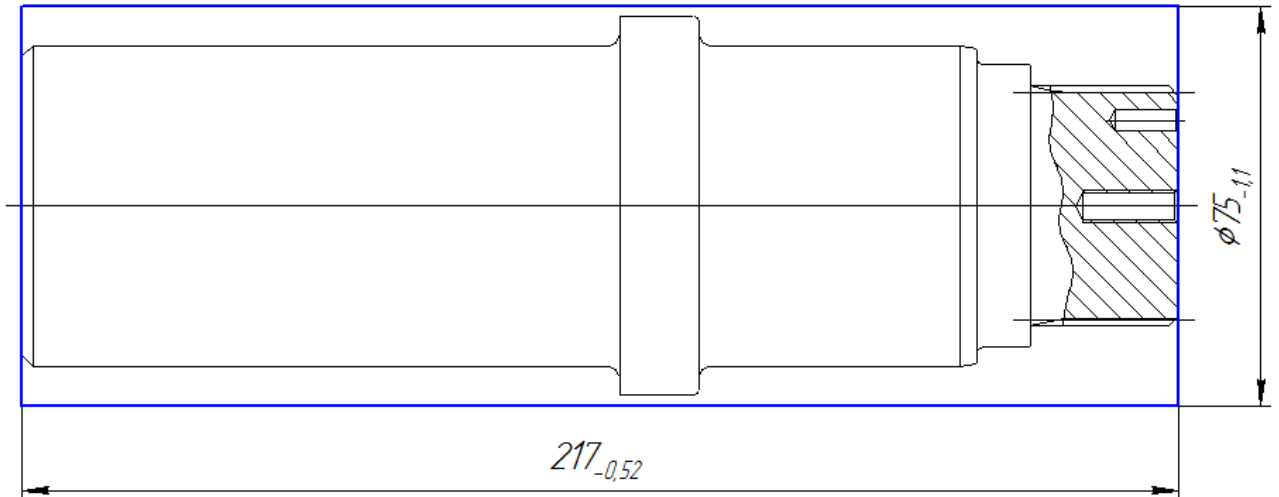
Ескіз заготовки прокат виготовлений розрізанням різцем
